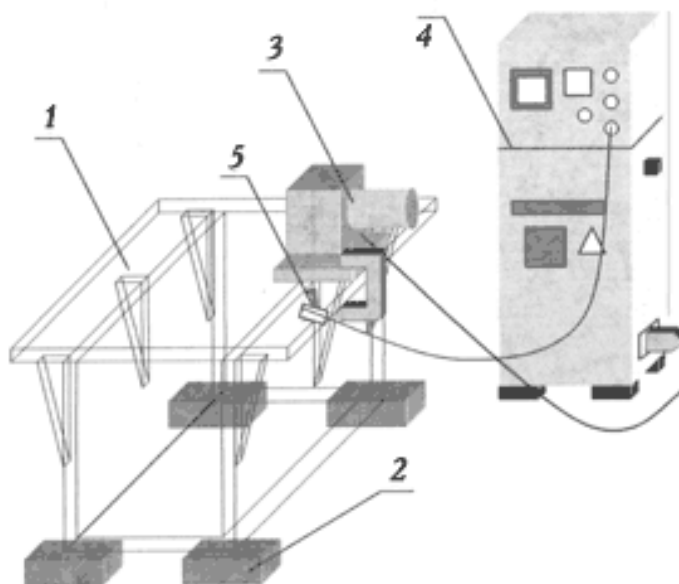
Схема установки для виброобработки сварных конструкций
